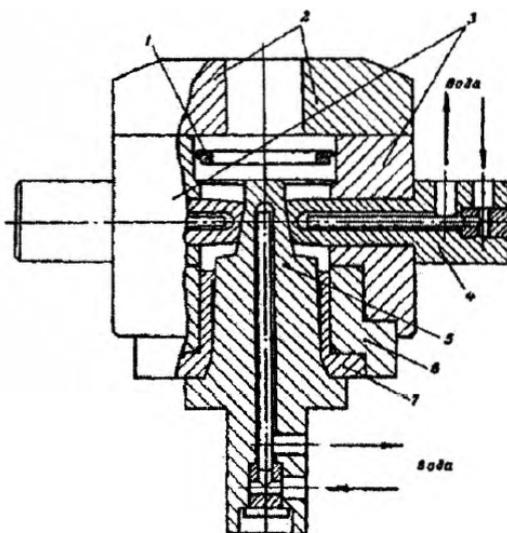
Кокиль для отливки поршня по технологии «дно вверх»
